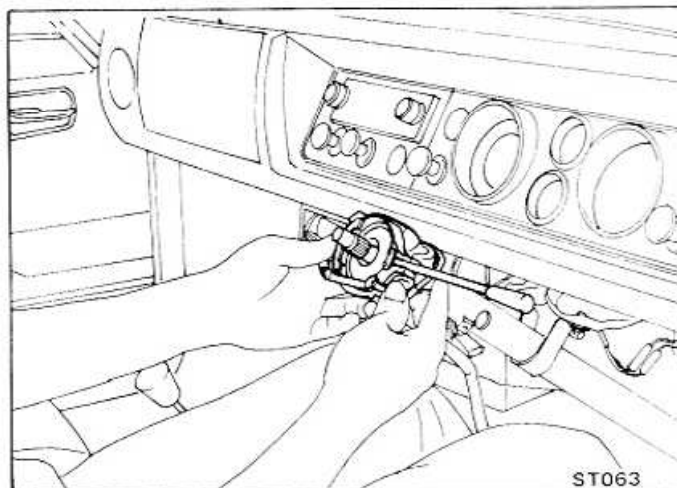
Dépose de l'ensemble d'interrupteur
